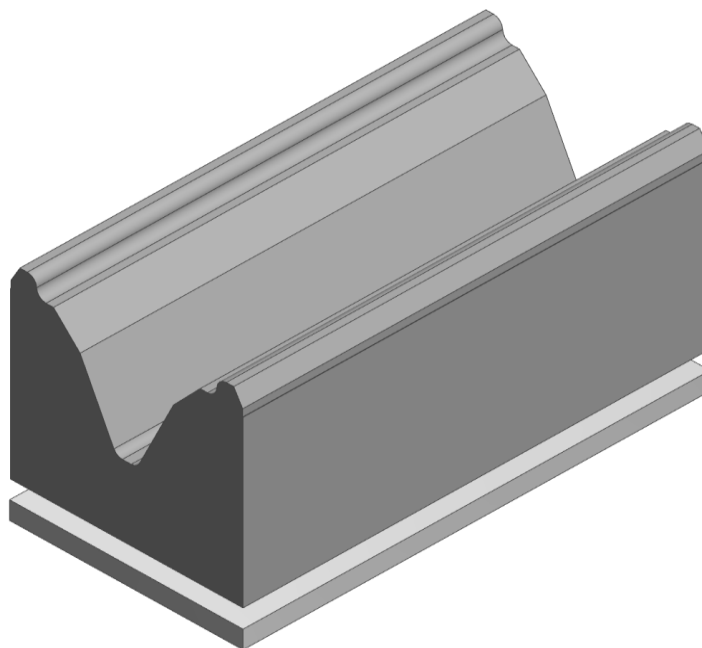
Model testovacího obrobku č.1. "zuby zaoblené zkosené".
